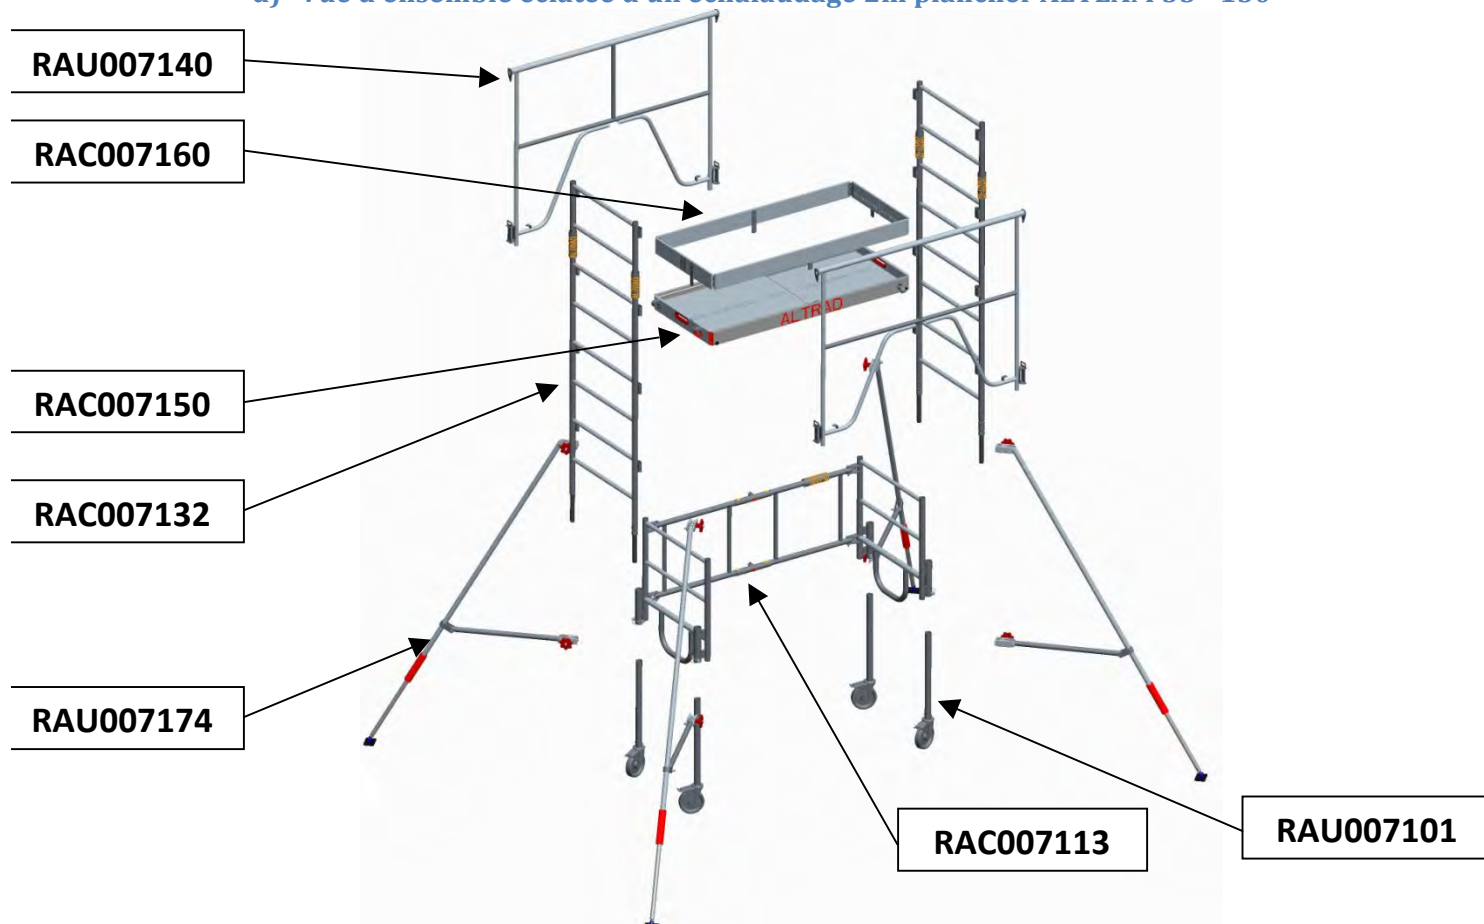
Vue d'ensemble éclatée d'un échafaudage 2m plancher (ALTEAM 35 - 150)
